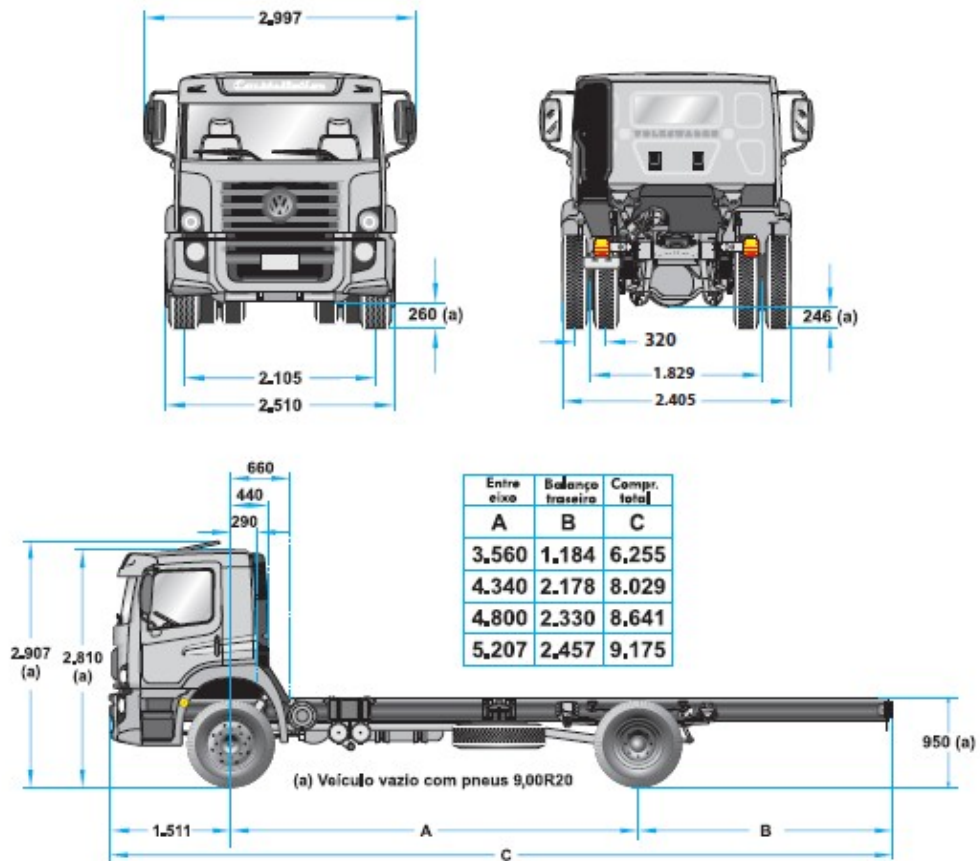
Dimensões Principais (mm) WV Constellation 13-180 e 15-180
